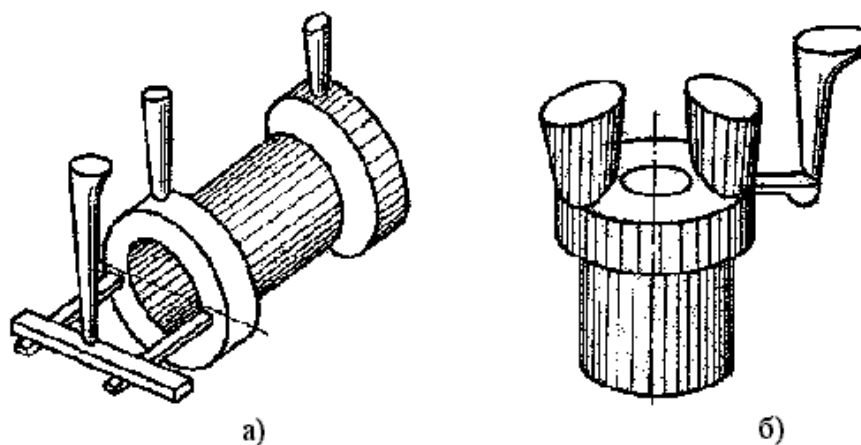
Эскизы готовых отливок с литниковой системой: а – отливка из чугуна; б – отливка из стали
